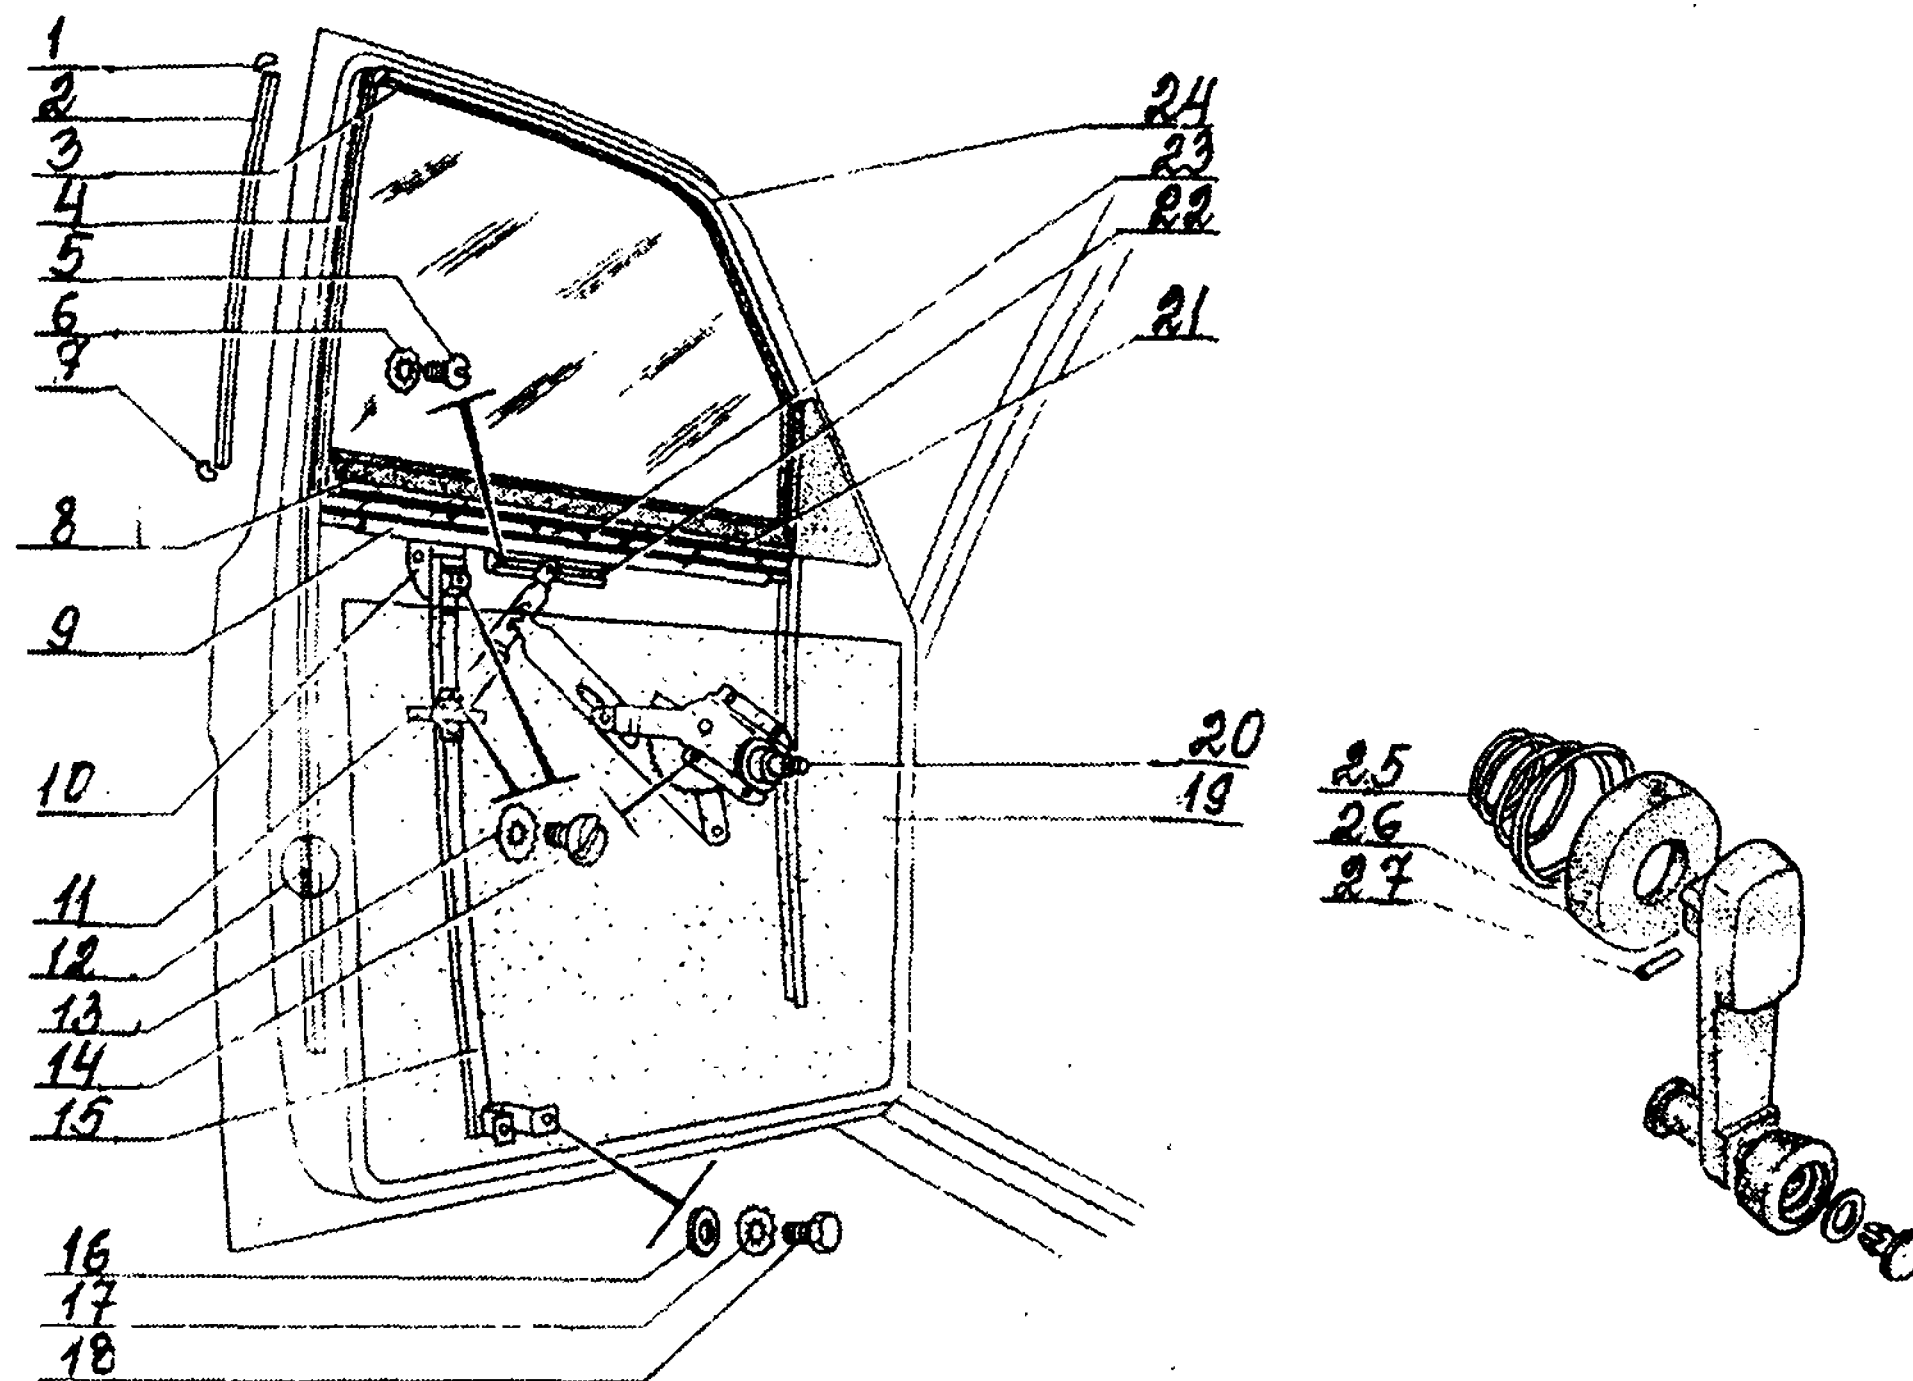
Дверь передняя, стеклоподъемник и его установка: 1 - муфта; 2 - окантовка; 3 - желобок верхний; 4 - желобок задний; 5 - винт; 6 - шайба пружинная; 7 - муфта; 8 - уплотнитель стекла; 9 - обойма стекла; 10 - держатель с камнями; 11 - кулиса нижняя; 12 - соединитель; 13 - шайба пружинная; 14 - винт крепления кулисы нижней; 15 - направляющая; 16 - шайба плоская; 17 - шайба пружинная; 18 - болт крепления направляющей; 19 - заклепка двери; 20 - стеклоподъемник передней двери; 21 - стекло опускающее; 22 - кулиса верхняя; 23 - держатель уплотнителя; 24 - окантовка верхняя; 25 - пружина натяжная; 26 - розетка ручки стеклоподъемника; 27 - штифт
